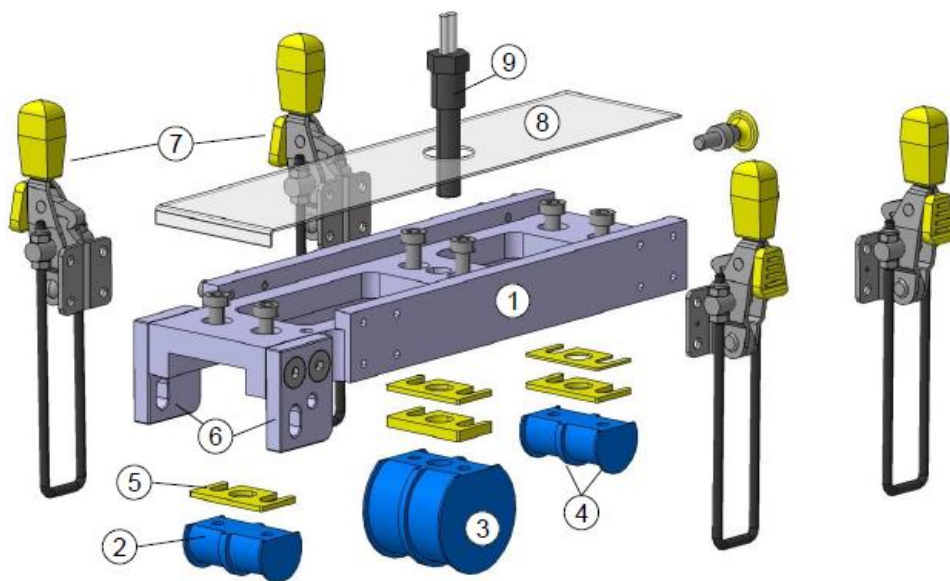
Komponenten der Werkzeugoberseite (Explosionsansicht)
